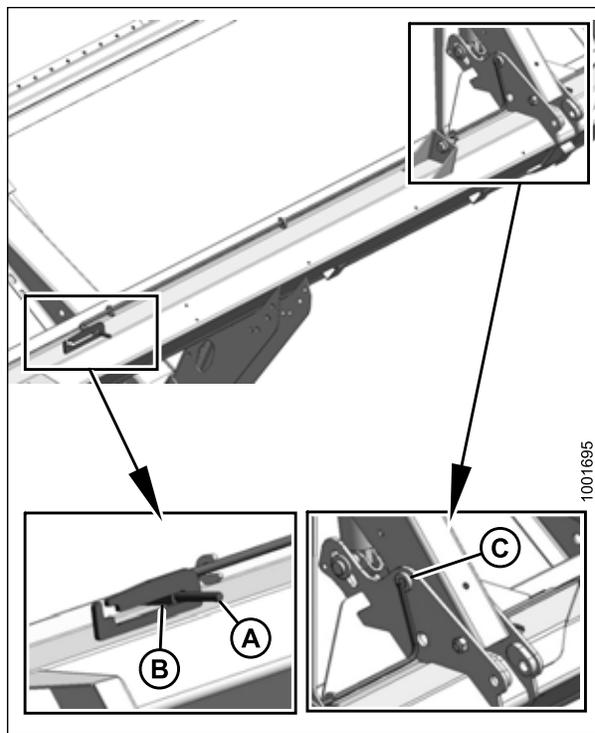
Предохранительный упор подбирающего мотовила — центральный рычаг
